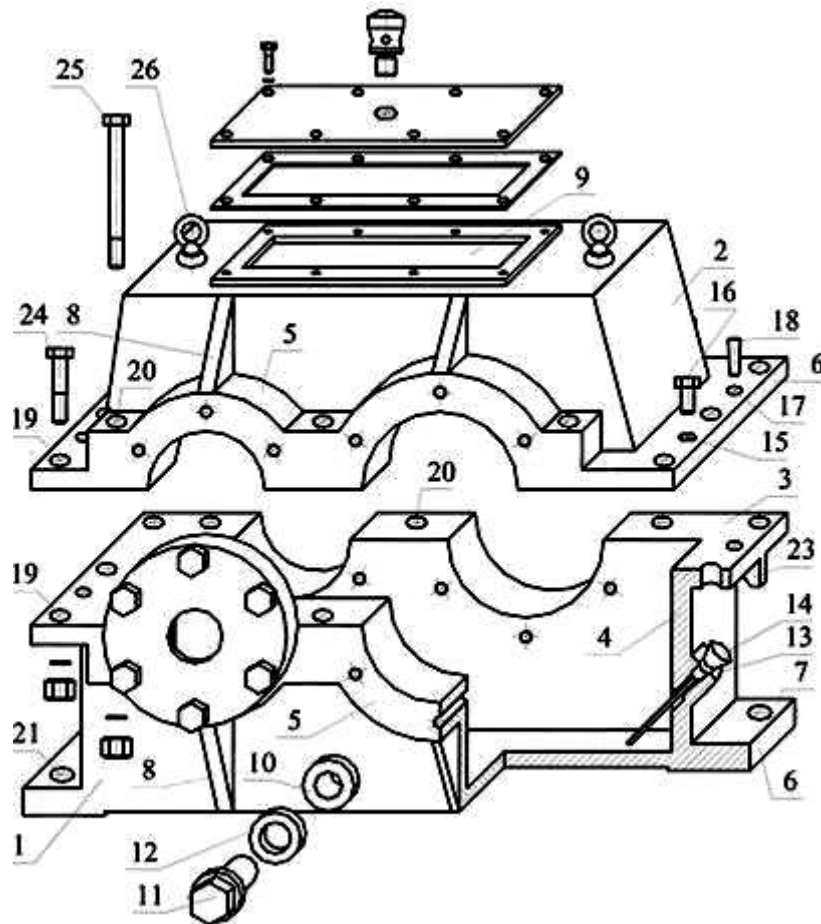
конструктивне оформлення литого рознімного корпусу редуктора.
